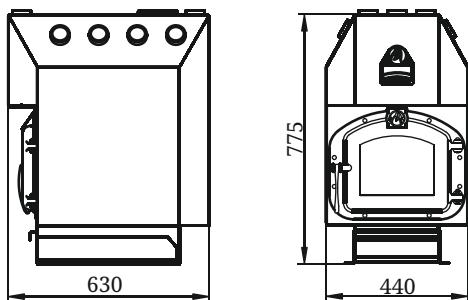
Габаритные размеры печи «Инженер» с выходом трубы вверх
